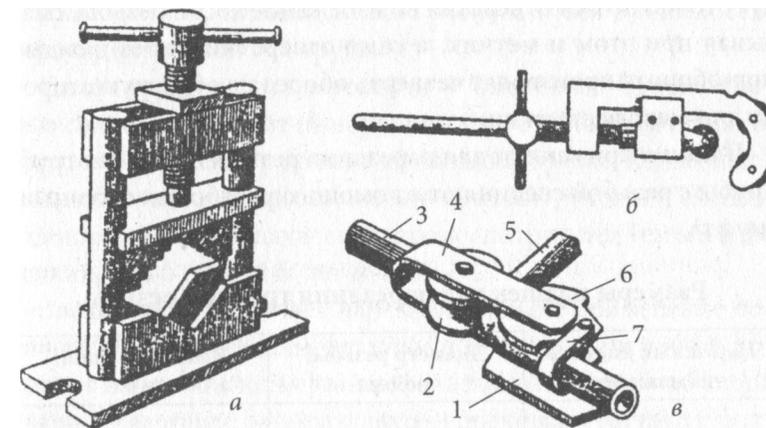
Инструменты для работы с трубами: а — прижим; б — труборез; 3 - стационарный трубогиб Вольнова: 1 — плита; 2 — подвижный ролик; 3 — рукоятка; 4 — скоба; 5 — труба; 6 — ролик-шаблон; 7 — хомутик
